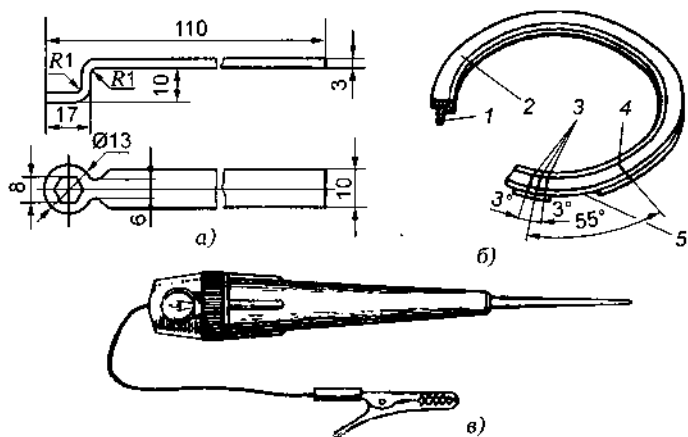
Приспособления для проверки угла замкнутого состояния контактов: *а* — специальный ключ; *б* — обойма со шкалой; *в* — автоиндикатор; 1 — обойма; 2 — шкала; 3 — контрольные риски; 4 — установочная риска; 5 — вырез в обойме для фиксатора крышки распределителя
